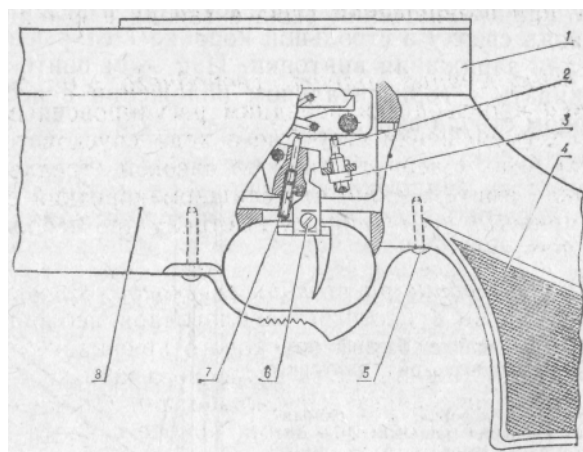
Спусковой механизм пневматической винтовки «312» (ГДР)
